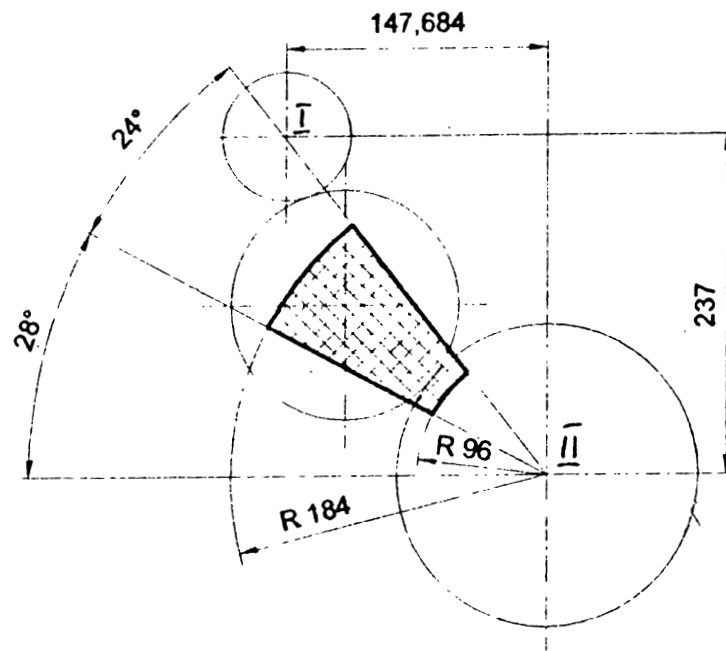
Чертеж для проверки возможности сцепления сменных зубчатых колес
